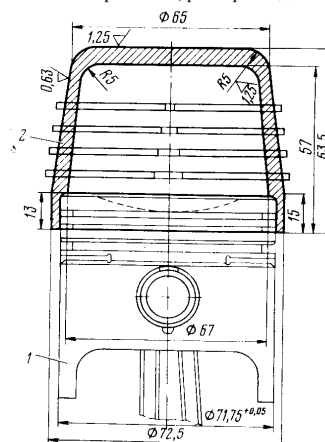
Оправка для надевания на поршень поршневых колец: 1 — поршень; 2 — оправка
